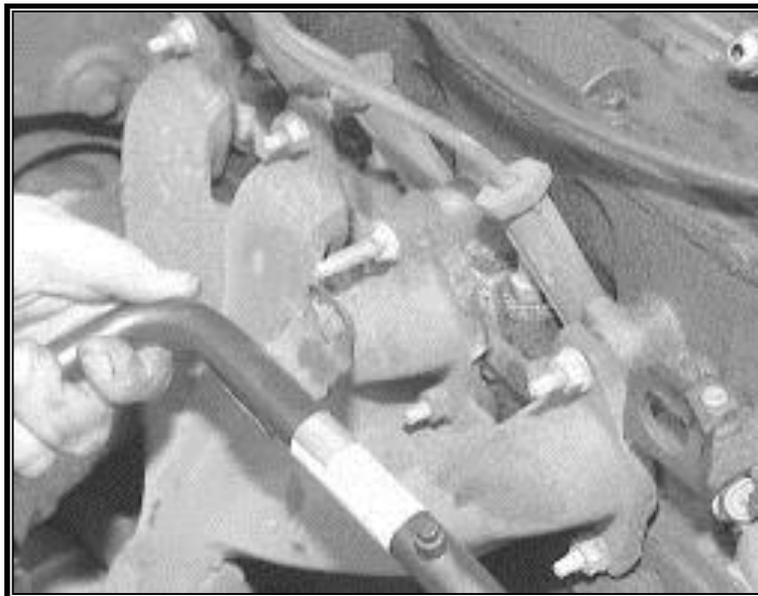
Tubería bypass de refrigeración. (AutoZone, 2018)
